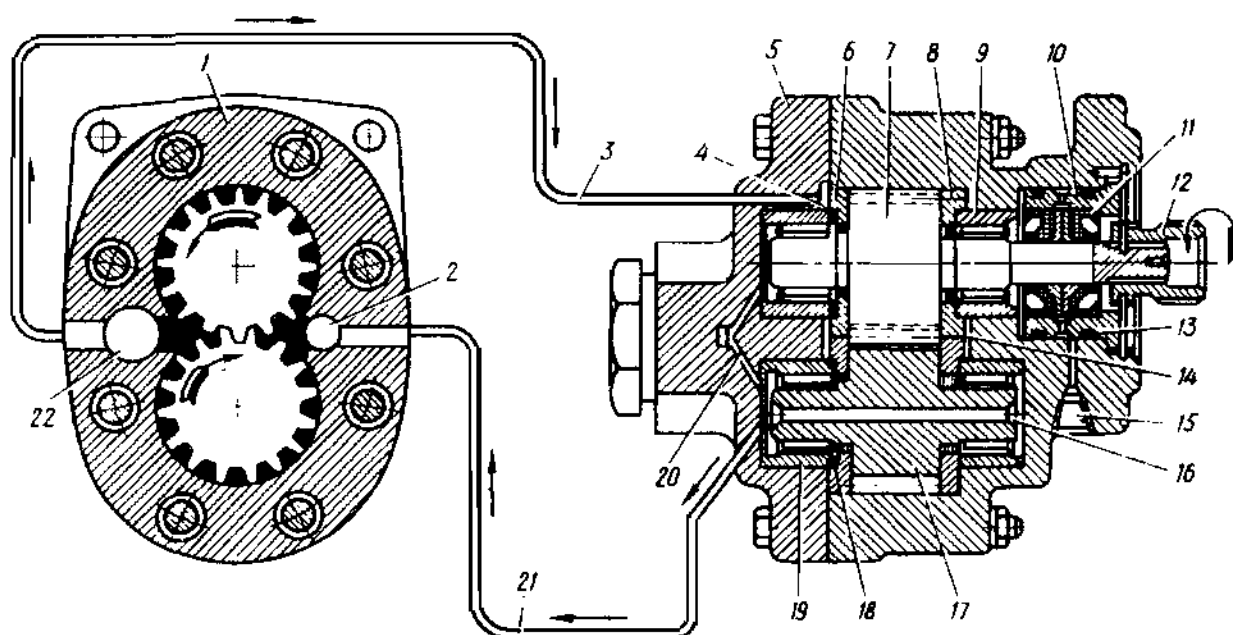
Насос шестеренчатый НШ-39М. Внешний вид
